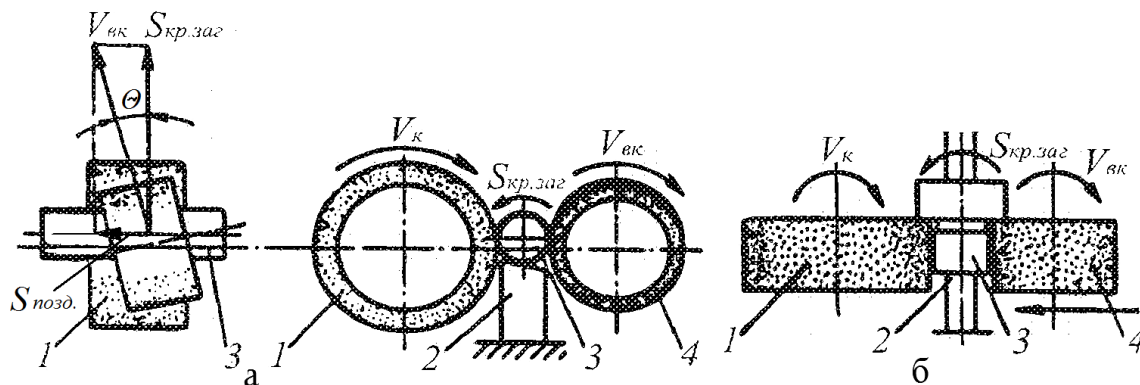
Схеми обробки заготовок на безцентрово-шліфувальних верстатах
